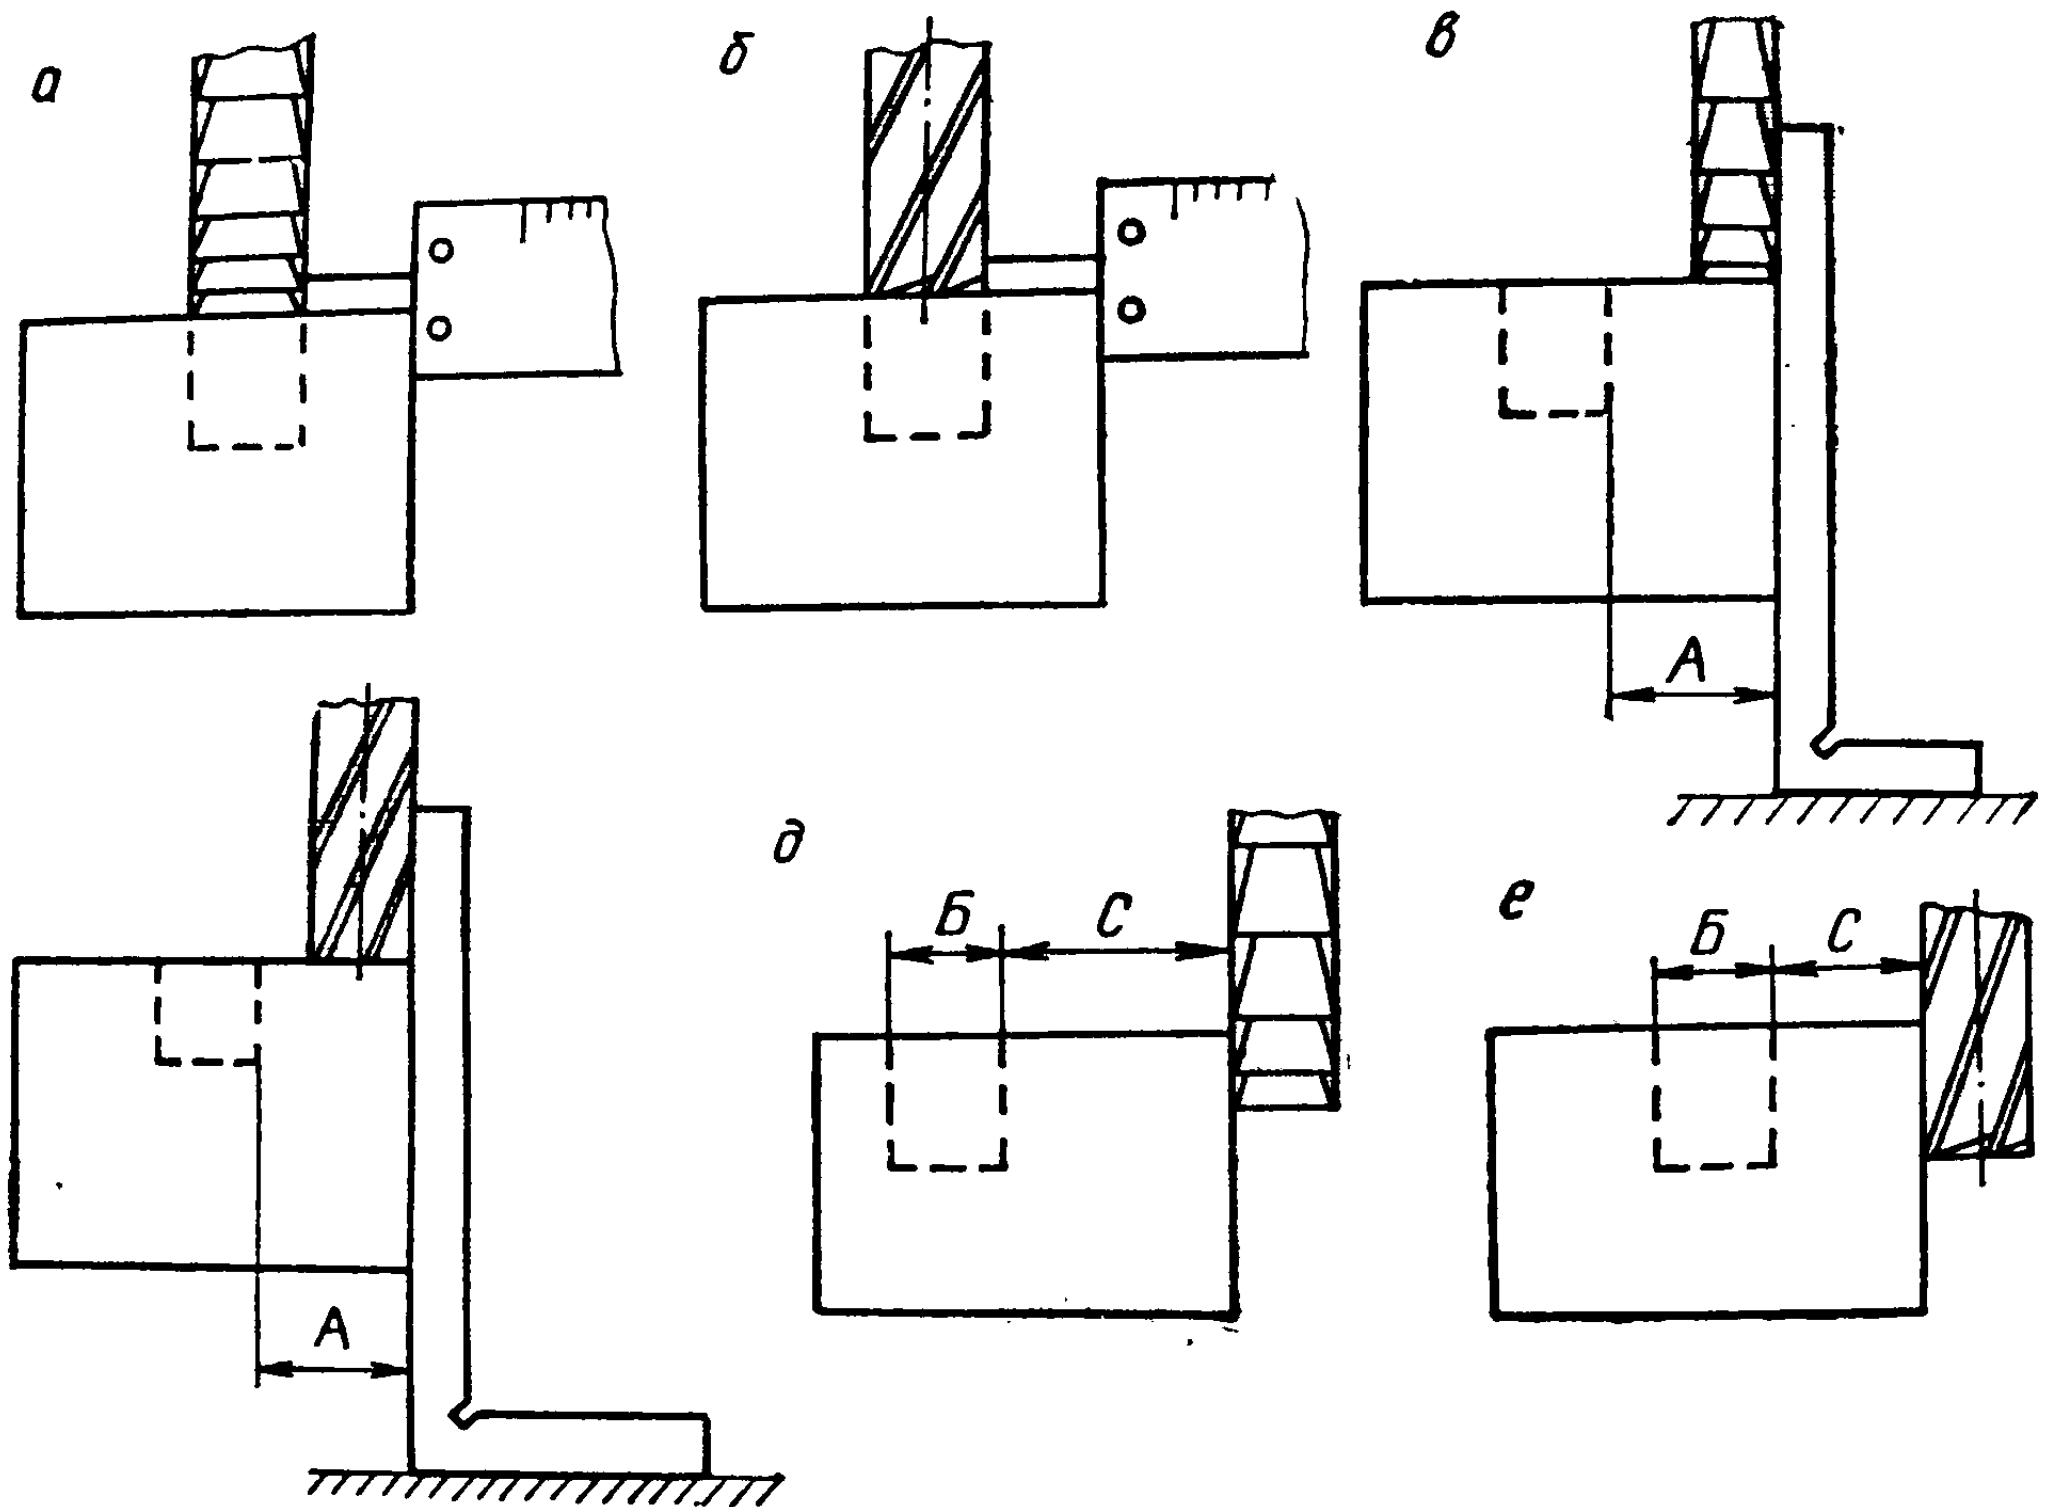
Способы установки заготовки относительно фрезы при фрезеровании прямоугольных пазов.
